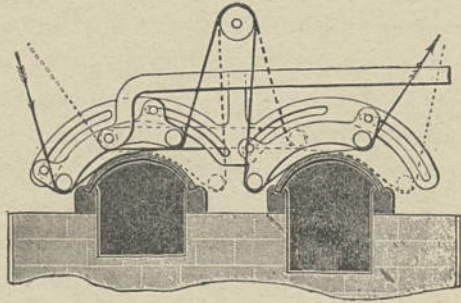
Grilleuse à plaques de Mather et Platt.
